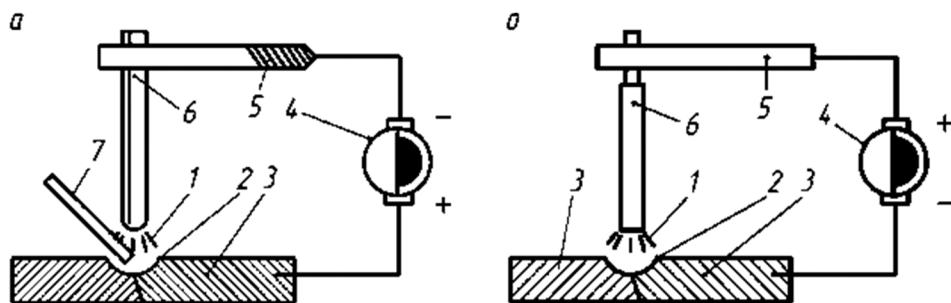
Схема ручного процесса дуговой сварки:
